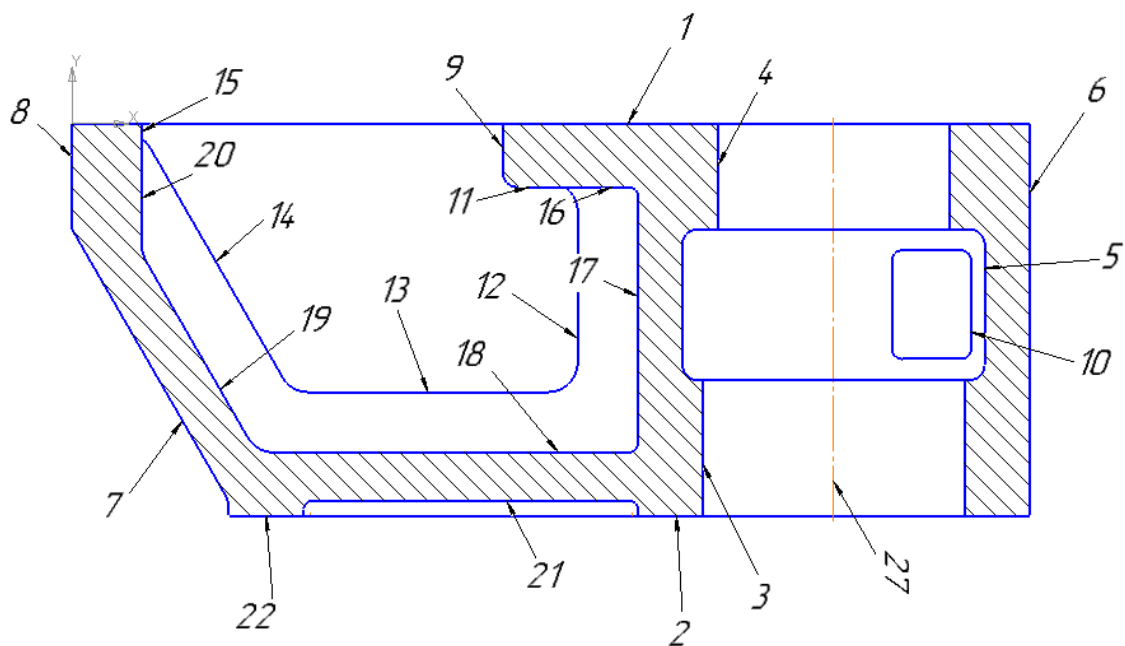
Спрощений ескіз заготовки, отриманої шляхом лиття у піщано-глинисті форми
